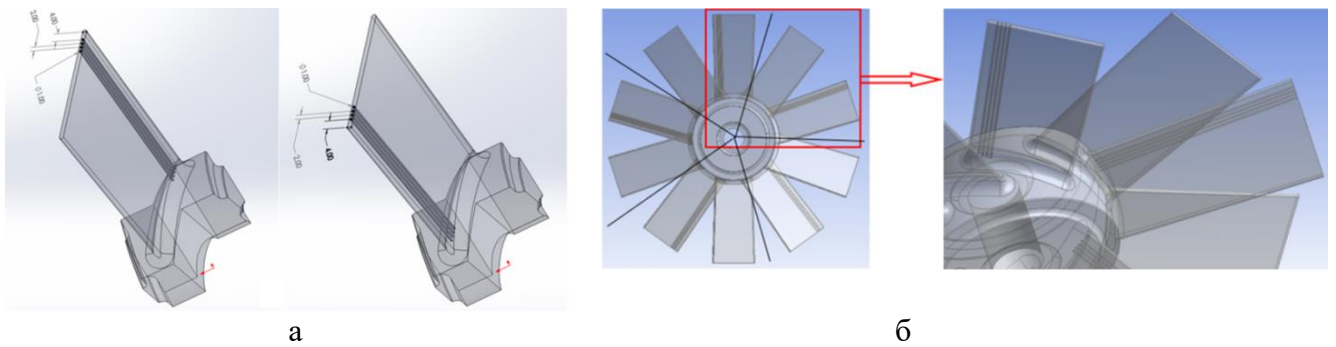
а, Варианты расположения отверстий на верхней кромке лопатки; б, Первая блочная модель при расположении отверстий на левой стороне
